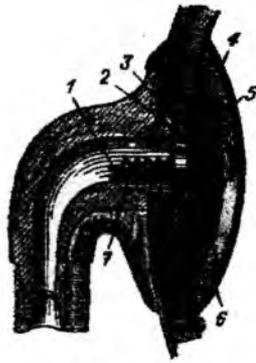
Запобіжний клапан повітротелефонного вводу: 1- стопорна гайка зі шплінтом; 2- шкіряна прокладка; 3- корпус клапана; 4- тарілка клапана; 5- шкіряна прокладка; 6- повітря-направляючий шток; 7- пружина.
